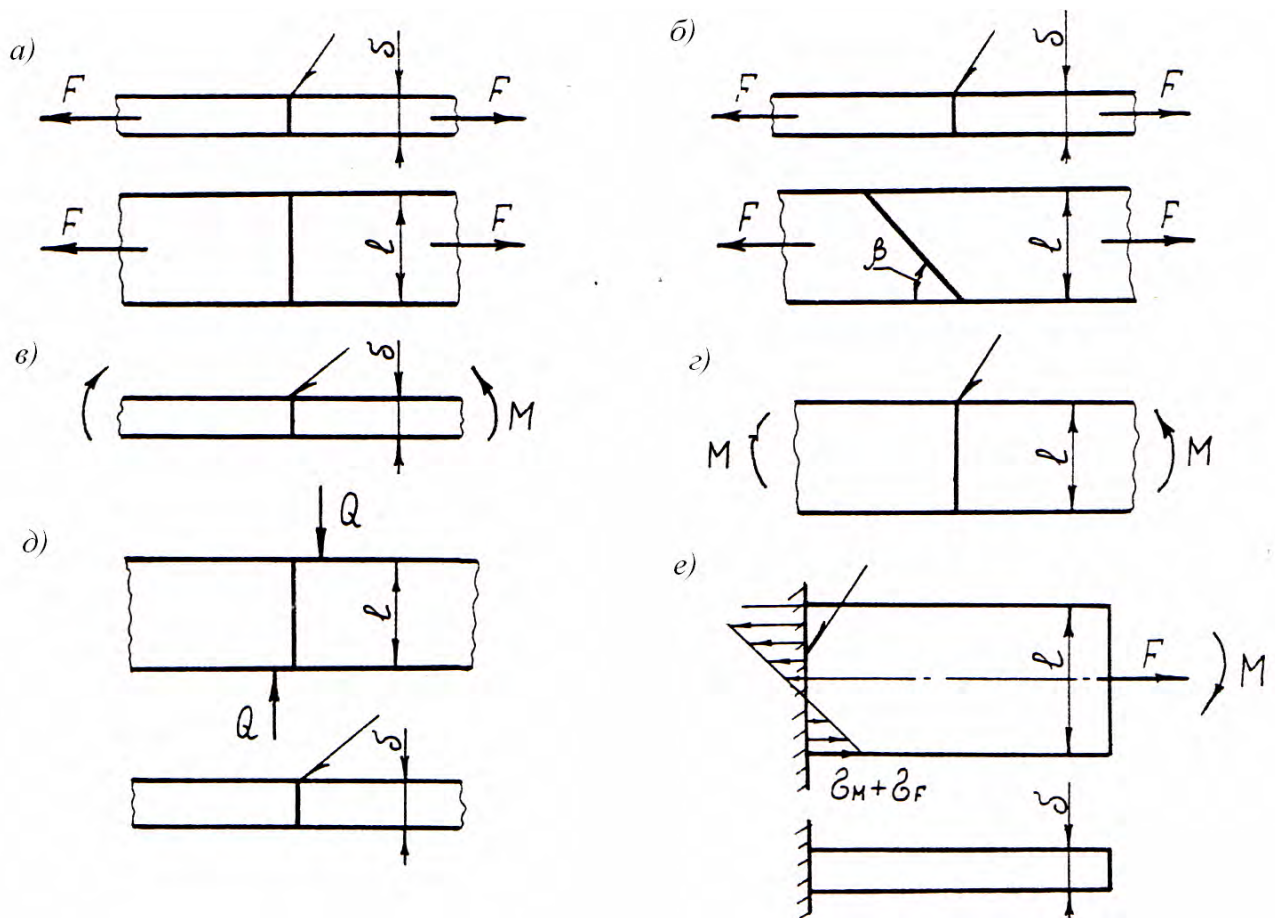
Варианты нагружения сварных стыковых соединений:
